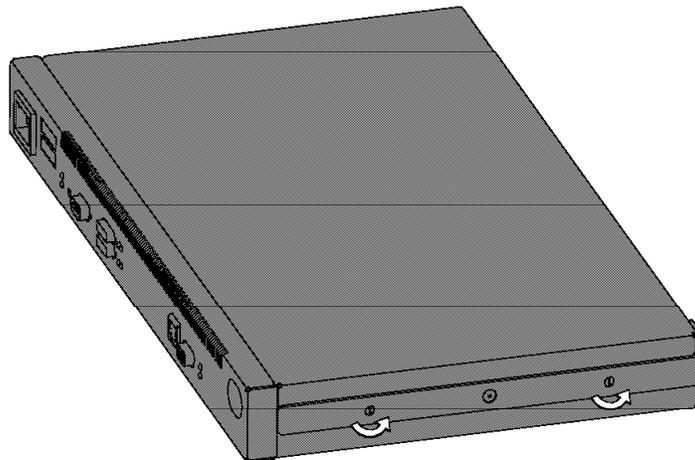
Remoção de Parafusos do Suporte de Montagem
